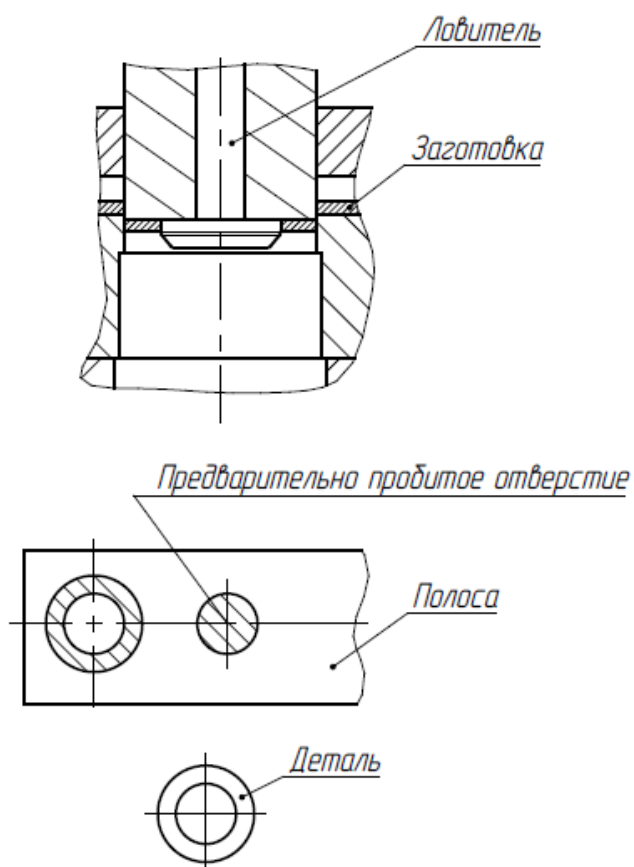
Штамп с ловителем для более точного расположения заготовки
